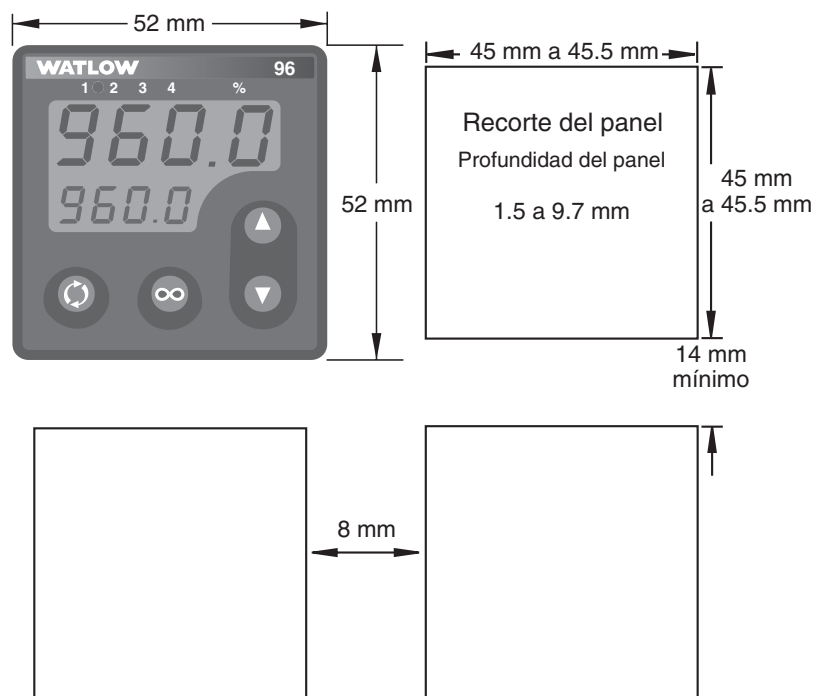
Dimensiones de los recortes de panel del controlador Serie 96.
